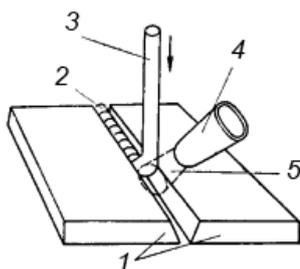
Схема сварки пластмасс нагретым газом с применением присадочного материала: 1 – свариваемые изделия, 2 – сварочный шов, 3 – присадочный материал, 4 – наконечник нагревателя, 5 – струя нагретого газа
